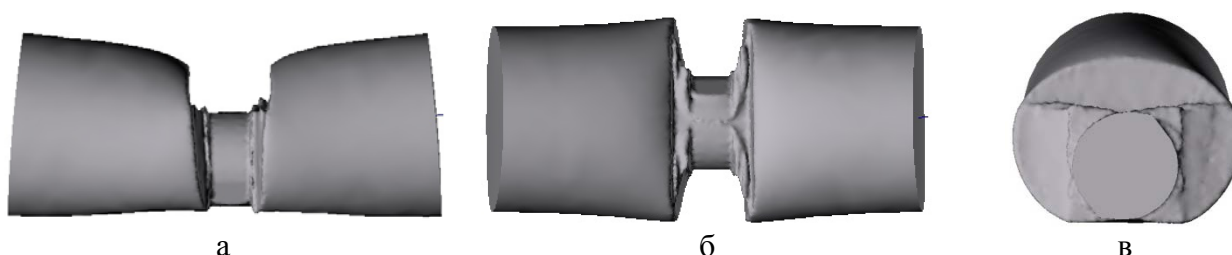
Загальний вигляд поковки колінчастого валу після відковування шатунної шийки: в – вид збоку; б – вид зверху; в – вигляд у перерізі шатунної шийки
